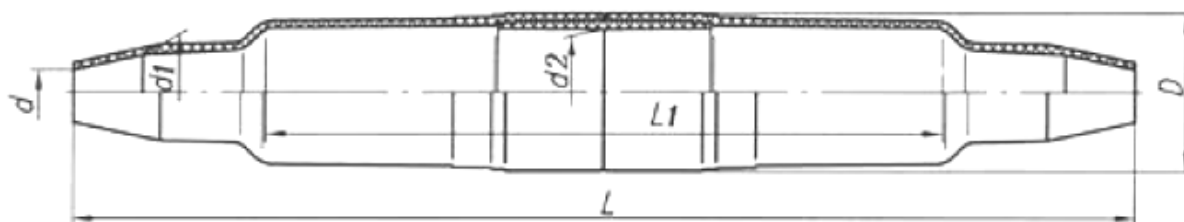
Размеры муфты МПП с корпусом из трёх деталей, двух полумуфт и втулки.
